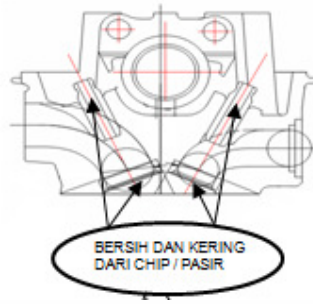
Proses OP 60 *Cylinder Head Machining
